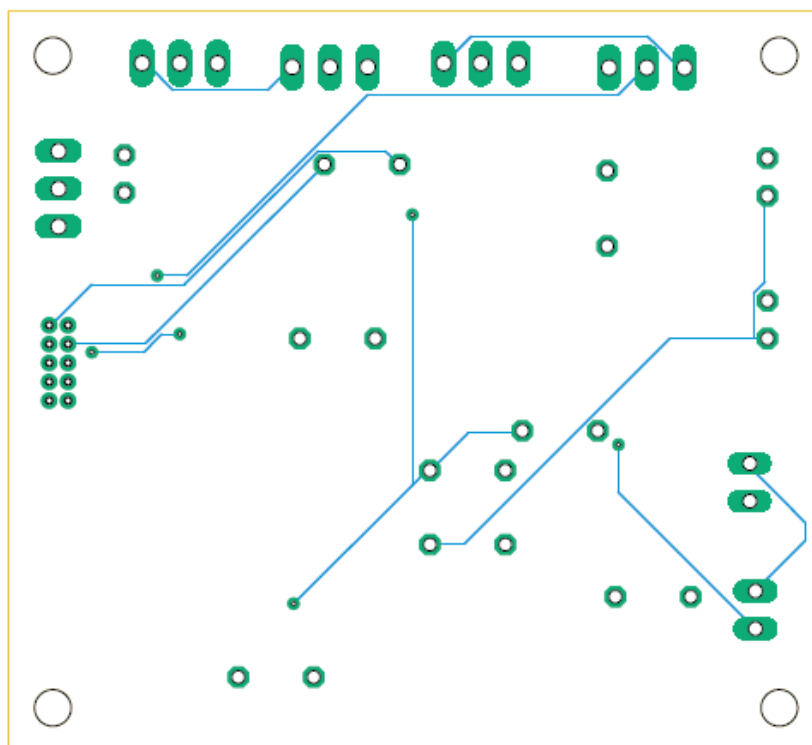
Diseño de la cara bottom de la PCB de calidad del agua salada
